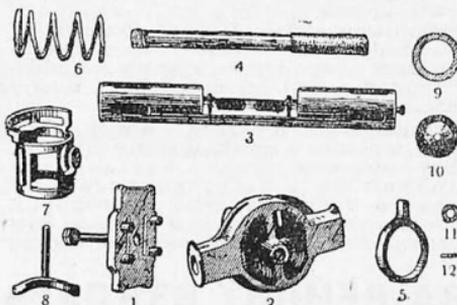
Части прибора, служащего для заливки коренных подшипников
